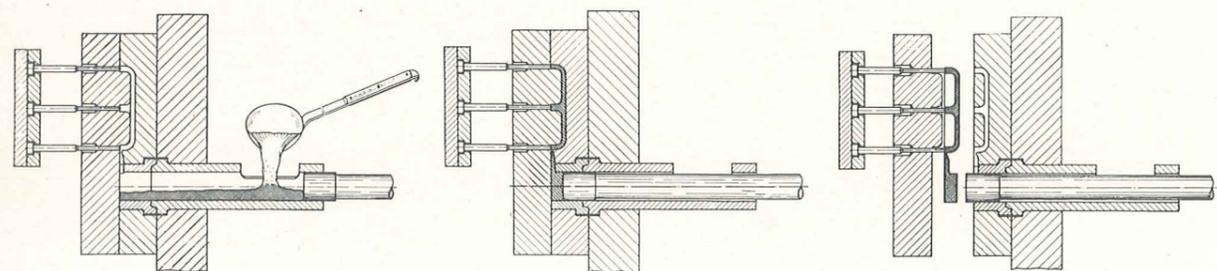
Füllzylinder mit Druckkolben und geschlossener Form beim Eingießen des Metalles einer Maschine mit waagerechter Druckkammer
